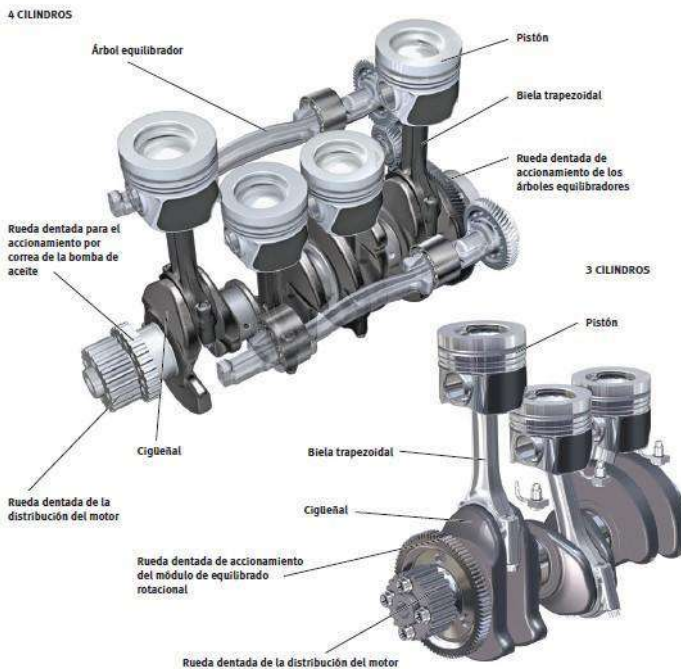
Conjunto móvil motor. Grupo VW motor company.
